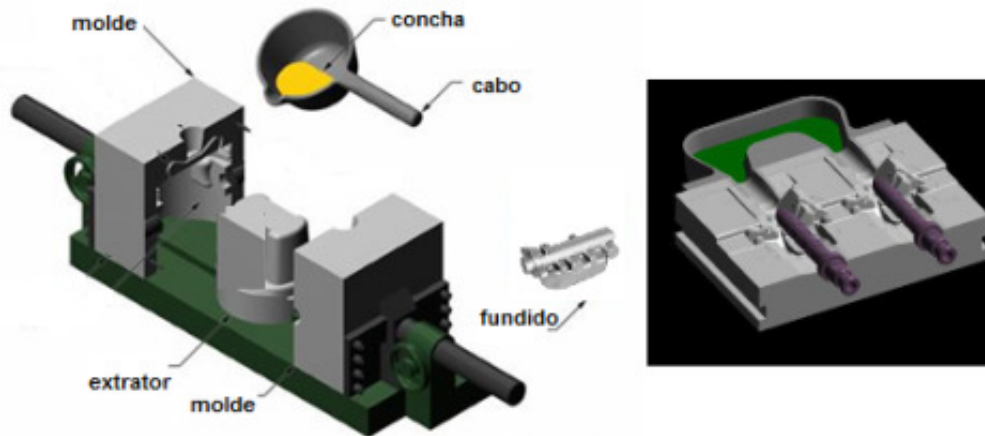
Máquina de coquilhar e molde usada no processo de fundição por gravidade.
